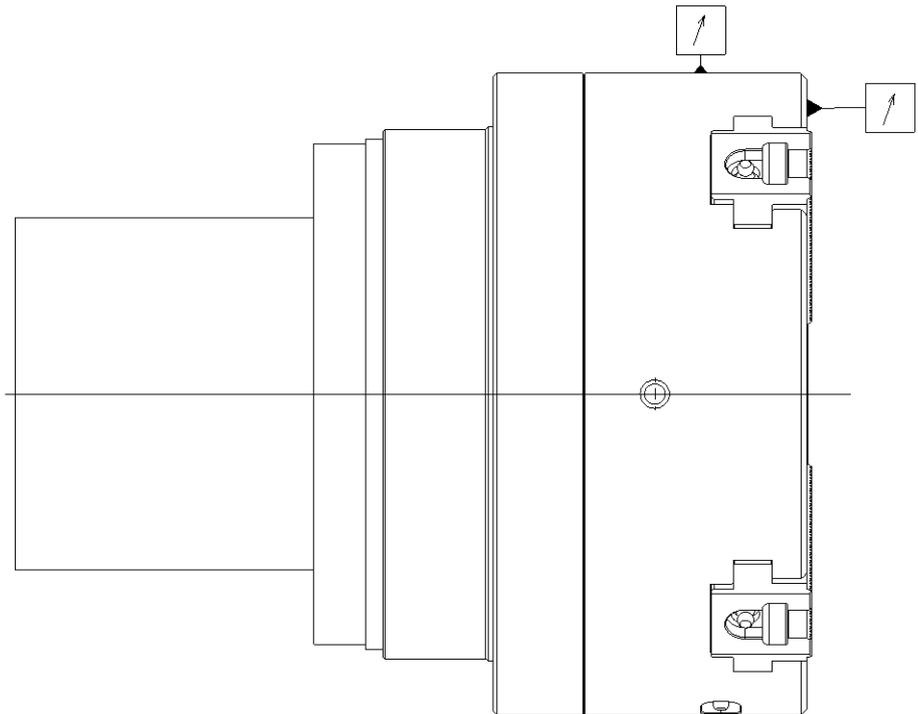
Mandrin de serrage monté sur une bride intermédiaire.
